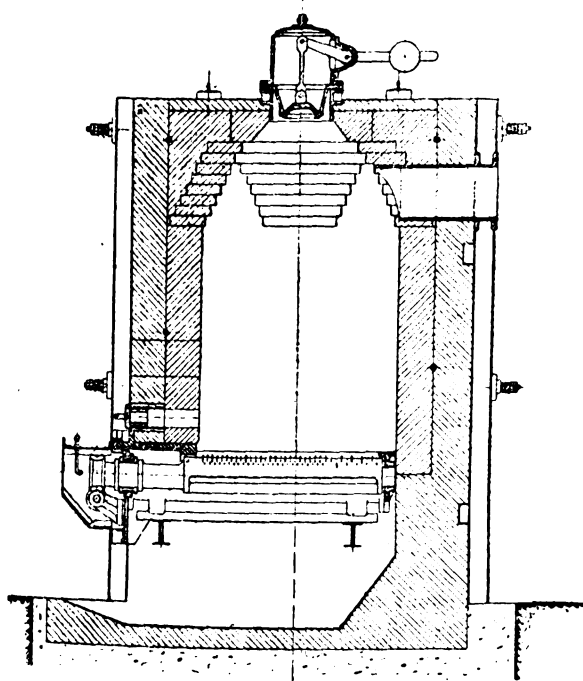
et 4. — Coupe longitudinale et coupe transversale d'un gazogène muni d'une grille Sauvageot.
